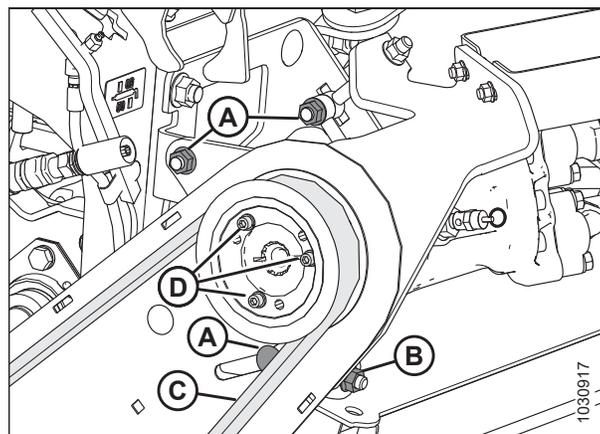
Ведущий шкив — Гидромотор привода плющилки
